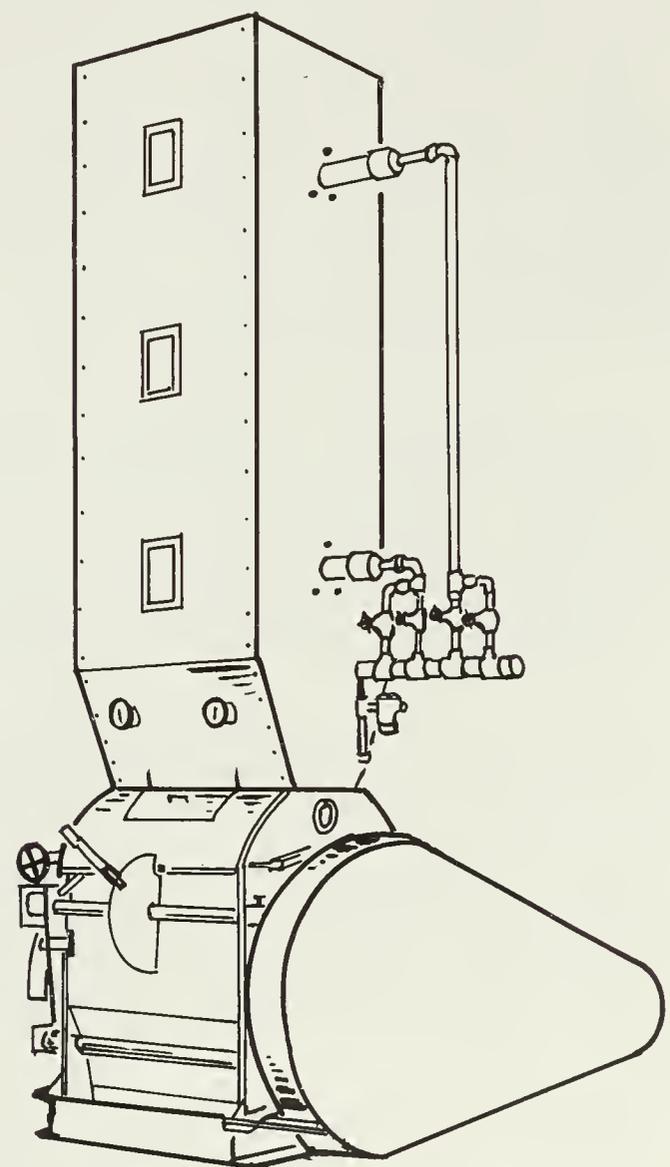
Chambre à vapeur accouplée à une rouleuse à grains. Source : Roskamp Manufacturing, Inc.
